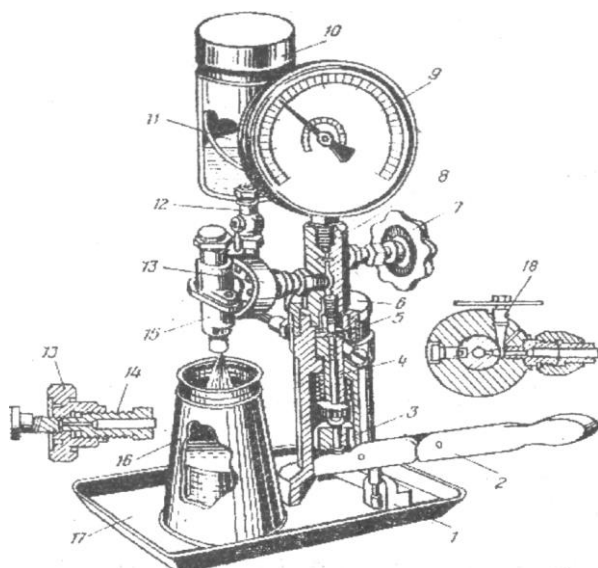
Прилад КИ-562 (КП-1609А) для вимірювання та регулювання форсунок: 1 – корпус; 2 – важіль; 3 – напрямна втулка; 4 – плунжерна пара; 5 – нагнітальний клапан; 6 – гайка корпуса; 7,13 – маховички; 8 – корпус розподільника; 9 – манометр; 10 – бачок; 11 – фільтр; 12 – кран; 14 – штуцер; 15 – форсунка; 16 – глушник; 17 – ємність; 18 – вентиль для випуску повітря.
